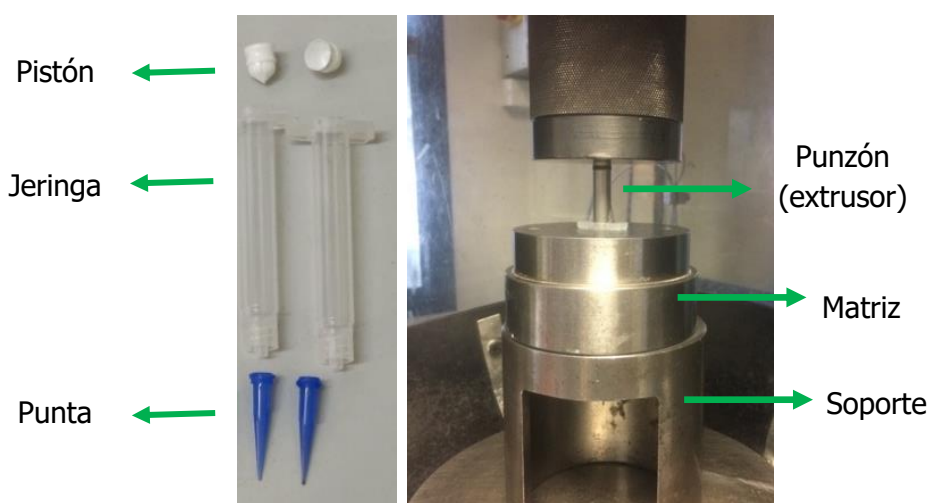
Utensilios de impresión 3D y acoplamiento del utillaje en la máquina de compresión AG-IS SHIMADZU.
